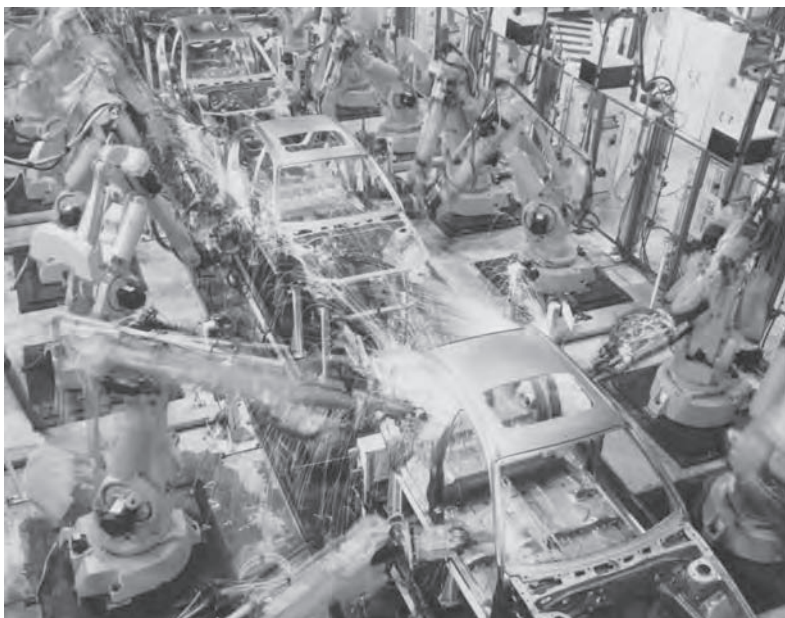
Línea de soldadura por puntos robotizada. (Cortesía ABB).
